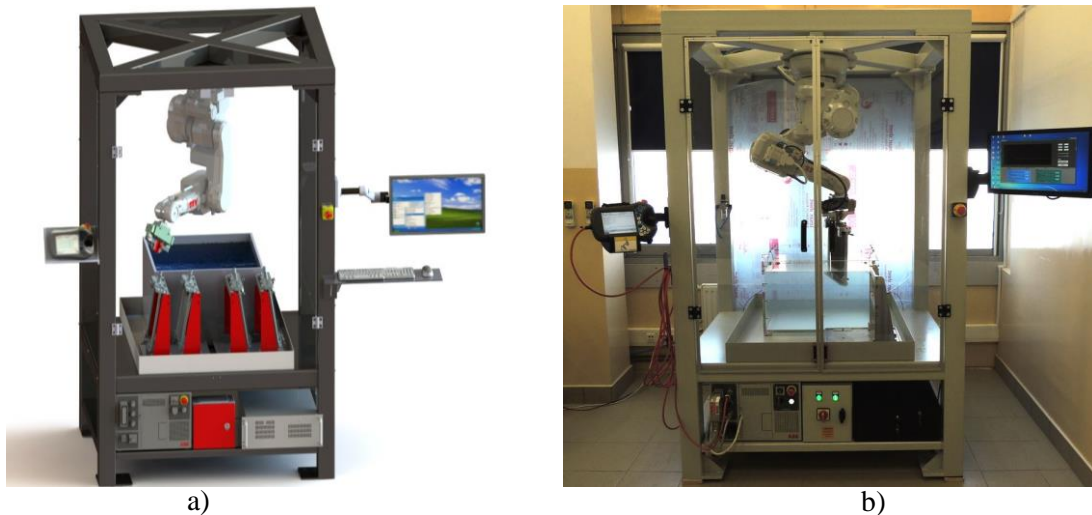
Zdjęcie stacji zrobotyzowanej podczas prac montażowych
